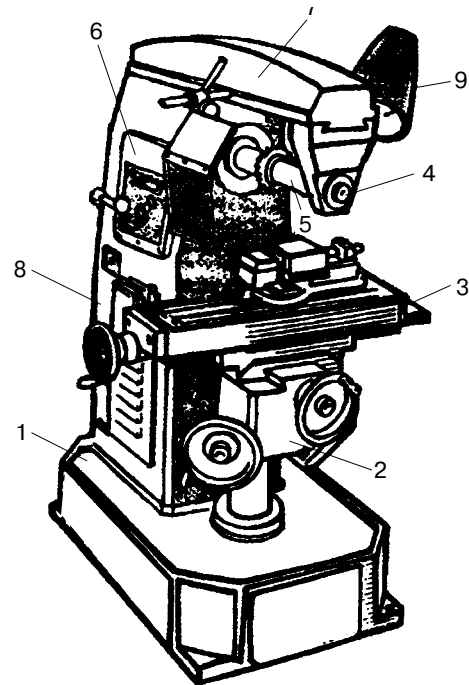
Общий вид фрезерного станка НГФ-110Ш4: 1 — основание; 2 — консоль; 3 — стол; 4 — шпиндель с оправкой; 5 — экран защитный; 6 — хобот с серьгой; 7 — стойка (станина); 8 — светильник местного освещения.
